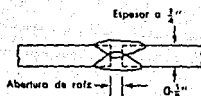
Junta a tope de acanaladura cuadrada soldada por ambos lados para que exista penetración y fusión completa.
